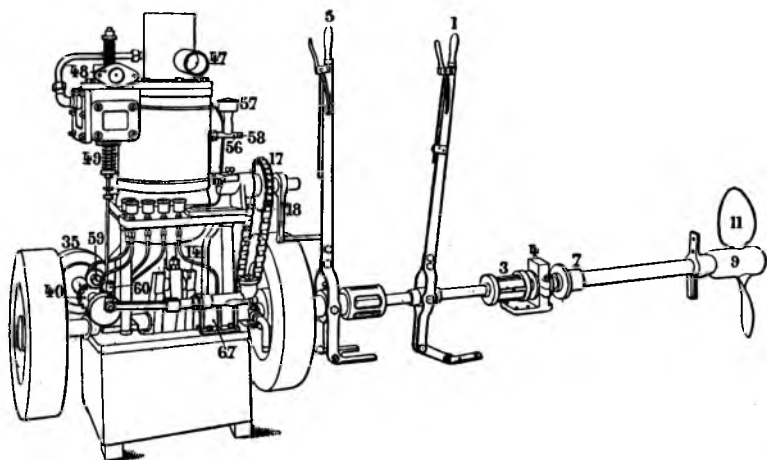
Пуск в ход двигателя посредством рукоятки 18, идущей по зубчатке 9.—3, упорный шариковый подшипник с направляющим подшипником 4 и набивкой 7.—5, рычаг сцепления.—47, накаленный шар, производящий вспышку, помещенный в кожухе.—48, всасывающий и выпускной клапаны.—56, 57 и 58, клапан, масленка и колпачек для смазки цилиндра.—35, центробежный регулятор.—40, кулачек выпускного клапана.—59, ролик для подъема выпускного клапана.—14, коленчатый вал.—67 водяной насос.—60, масленка на шатунах насоса.
